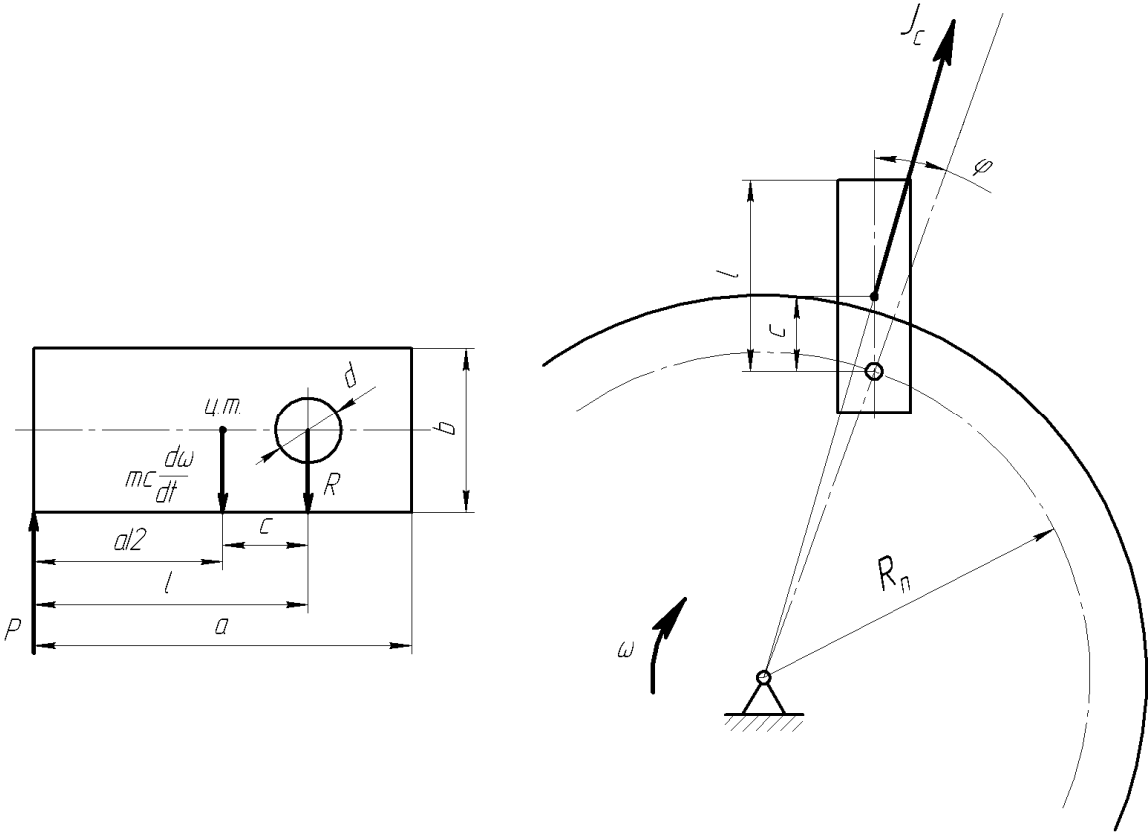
Схема для определения размеров молотка дробилки
